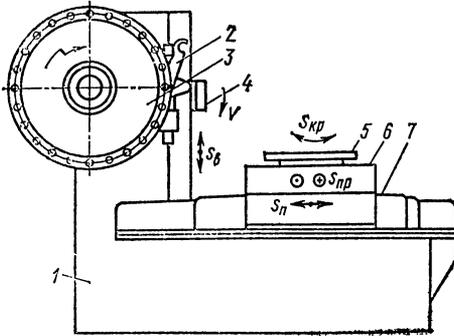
Общий вид фрезерно-сверлильно-расточного станка с инструментальным магазином
